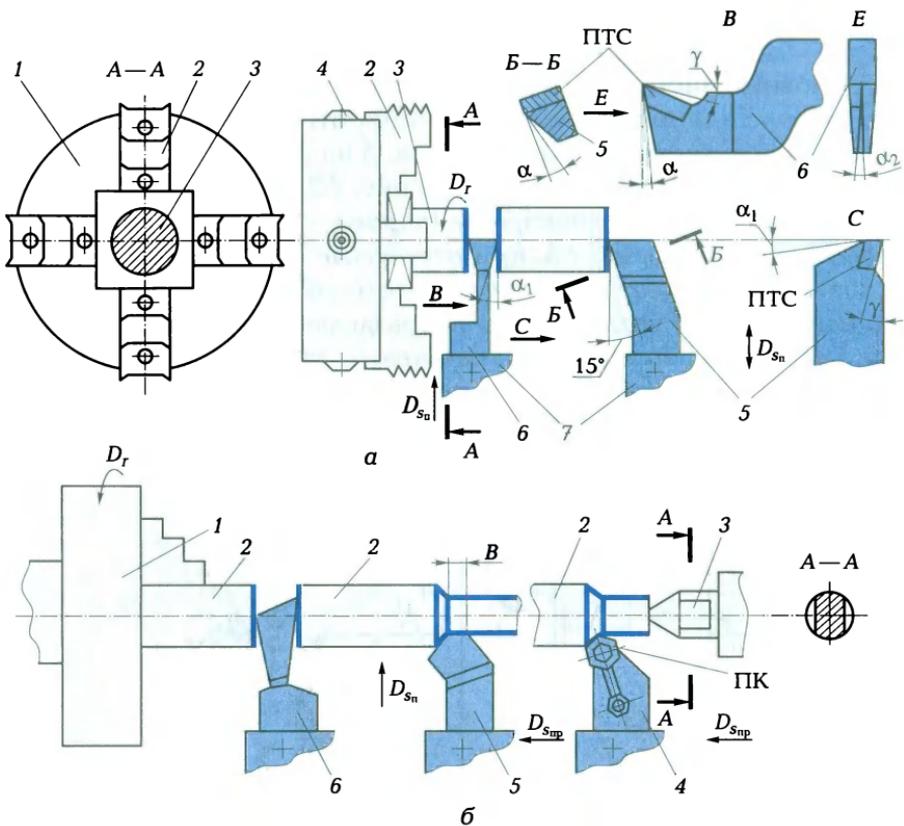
Схемы обработки на токарно-винторезном станке заготовок, закрепленных в патронах:
